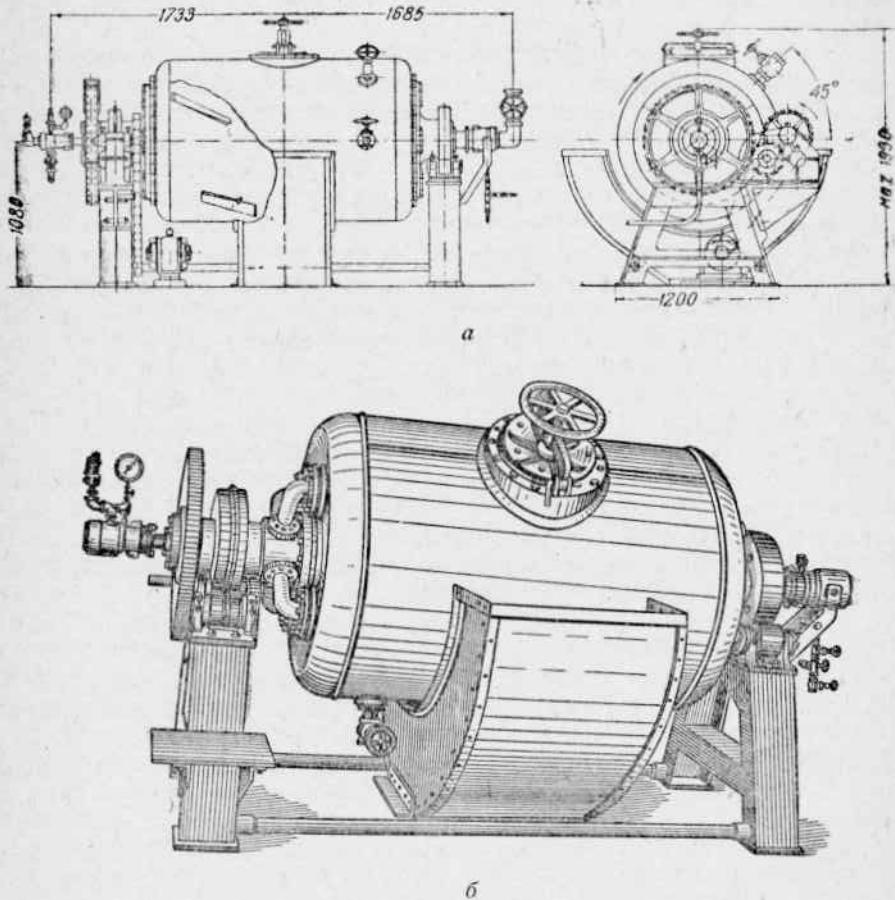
а, б: а — чертеж варочного аппарата; б — общий вид варочного аппарата
